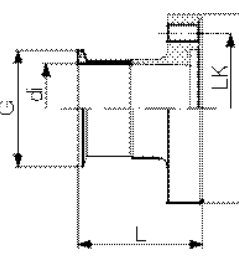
Dimensiones de la parte frontal del sensor DN 40...100
